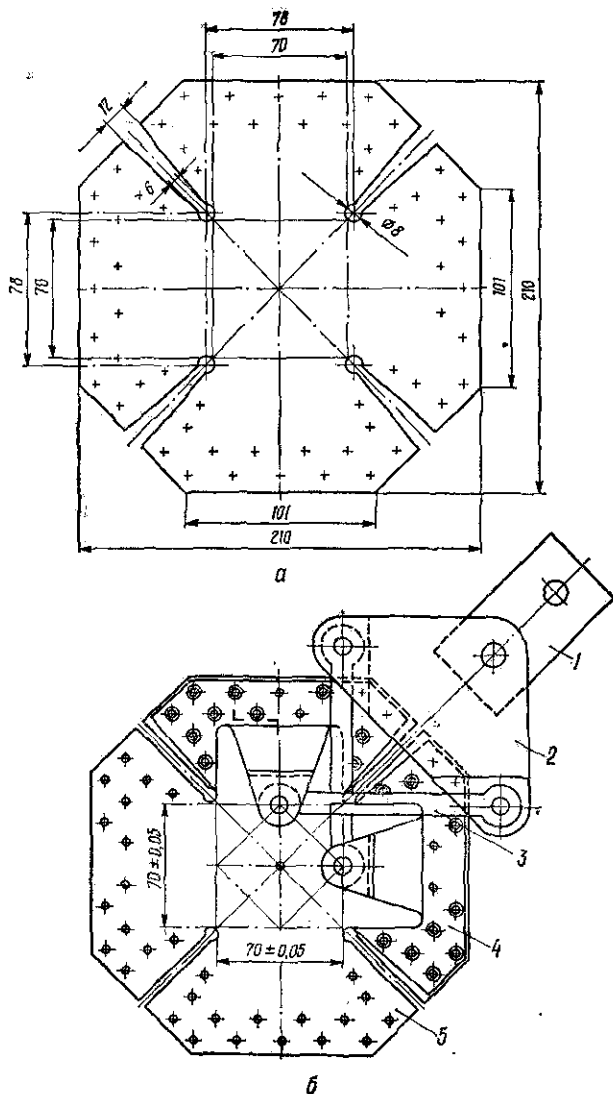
Образец с пропилами (а) и модифицированный шарнирный четырехзвенник (б) для испытаний КМ на сдвиг:
